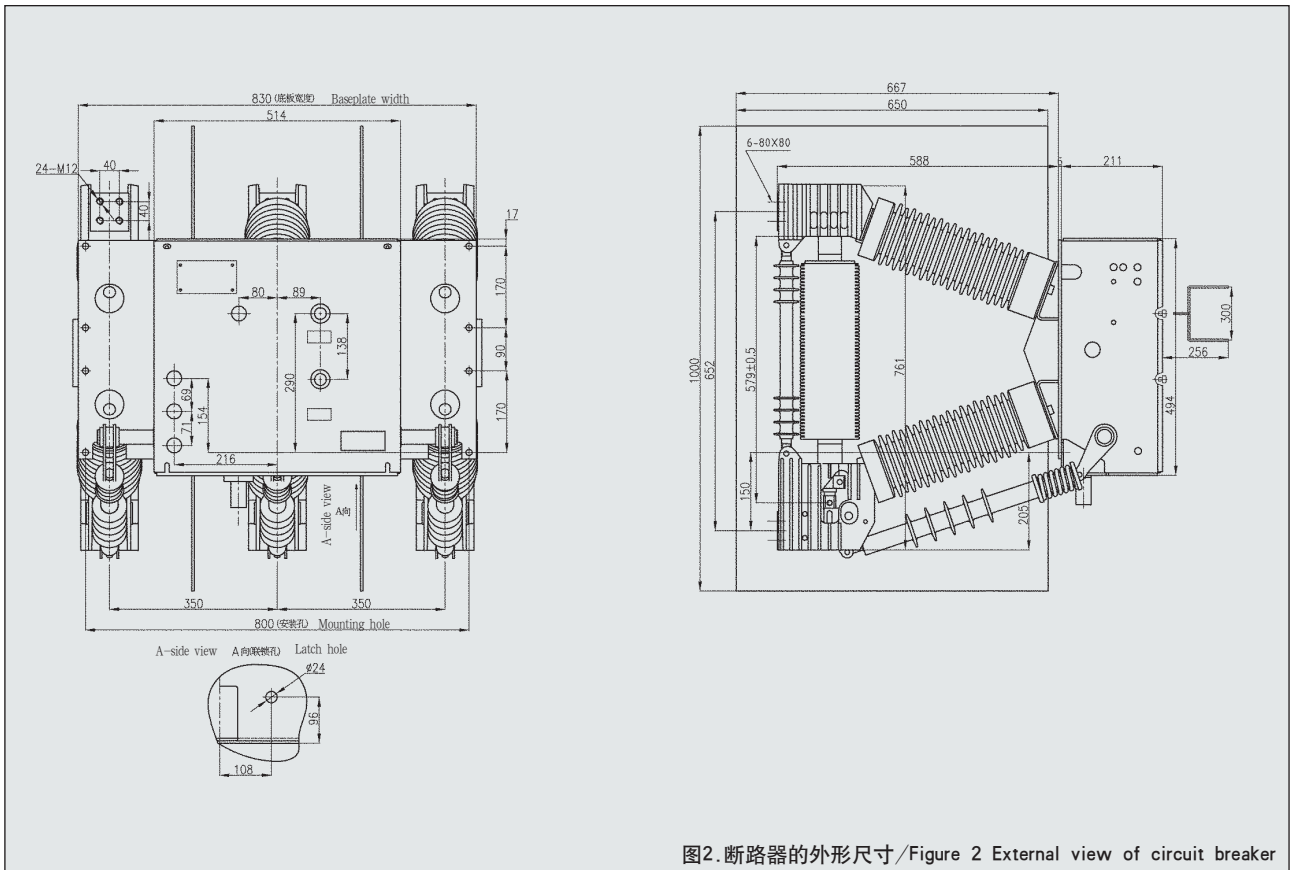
断路器的外形尺寸 / Figure 2 External view of circuit breaker
